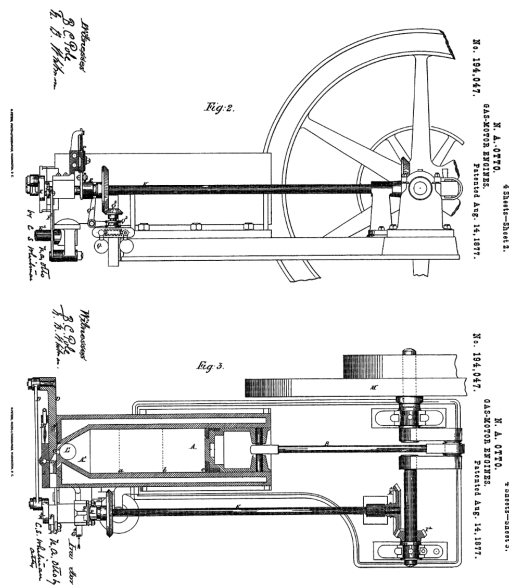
Dibujo de la patente de Nicolaus Otto del motor de gas. Fuente: "Motores de combustión interna alternativos" Prof. F. Payri, Prof. J. M. Desantes.
